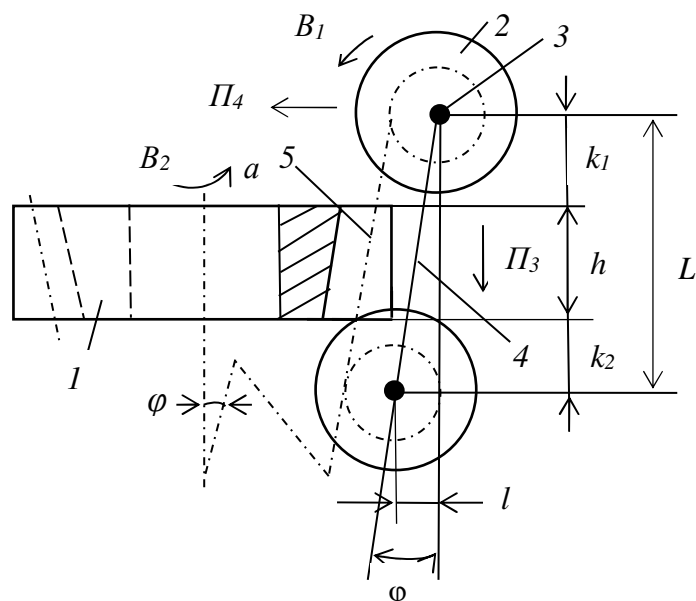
Способ фрезерования цилиндрических зубчатых колес с наклонными зубьями
